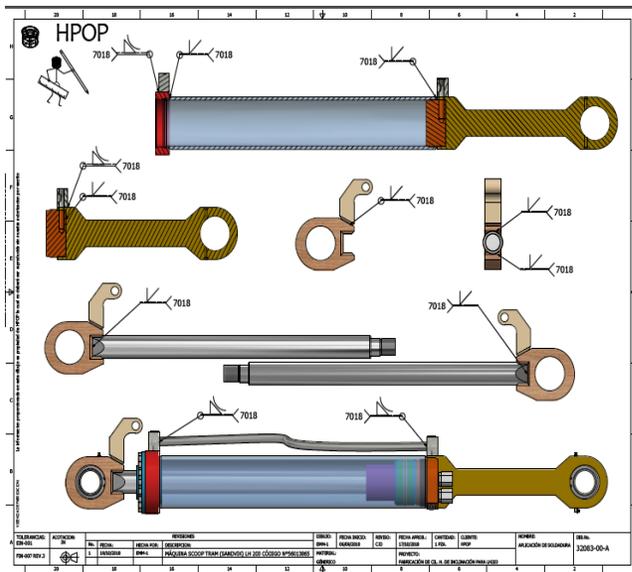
Dibujo del proceso de aplicación de soldadura del Cilindro Hidráulico con número de ingreso 32083
